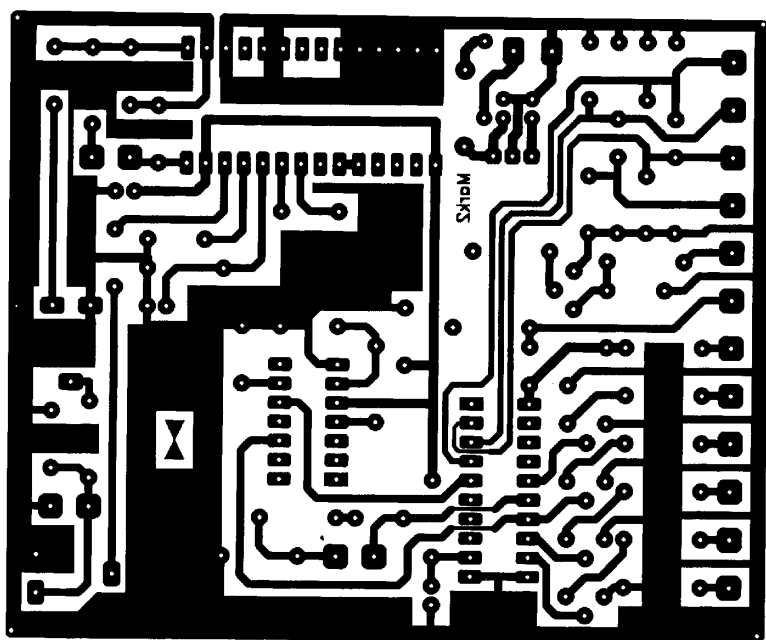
De print-layout in spiegelbeeld (dubbelzijdig).
